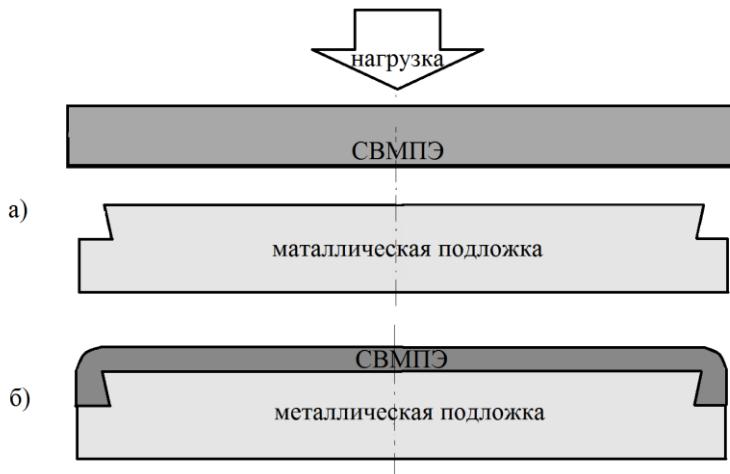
Схема соединения «металл-СВМПЭ»: а) схема соединения заготовок СВМПЭ и металла, б) готовое изделие.
